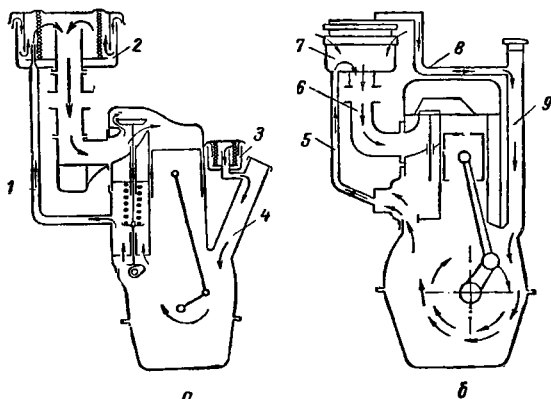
Схема принудительной вентиляции картера двигателей ЗИЛ-120(а) и ГАЗ-51 (б).
